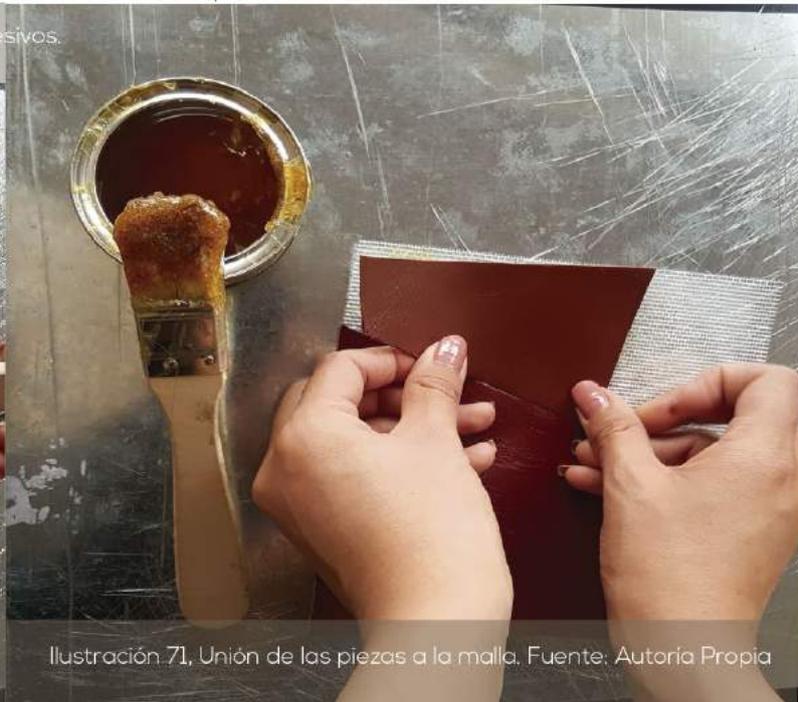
, Unión de las piezas a la malla. Fuente: Autoría Propia
